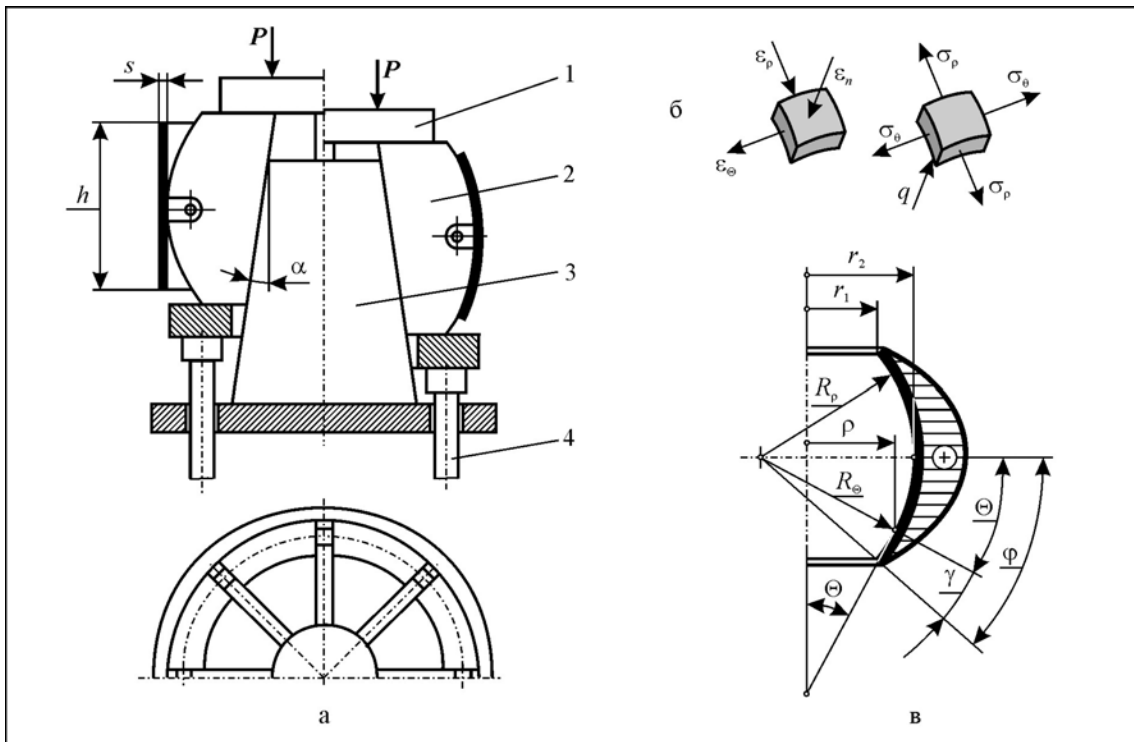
Штмп для кільцевого обтягування (а), механічна схема деформування (б) та епюра розподілу напружень (в): 1 – верхня рухома плита; 2 – розтискний пуансон; 3 – конусна оправка; 4 – штовхач
